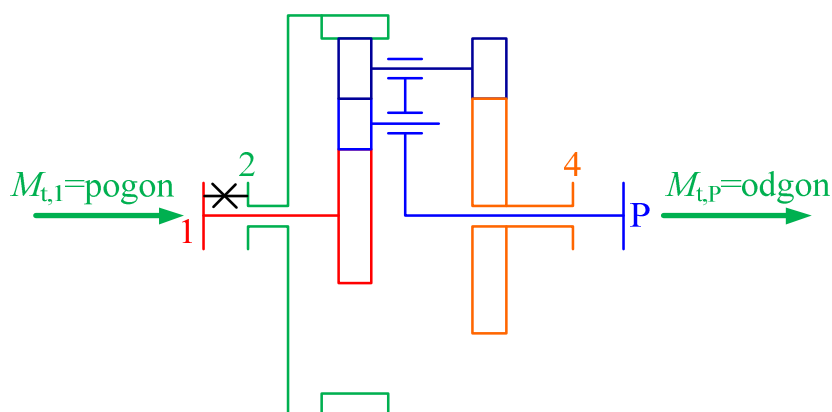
Prva prestava pri planetnem gonilu Ravigneaux [19]
